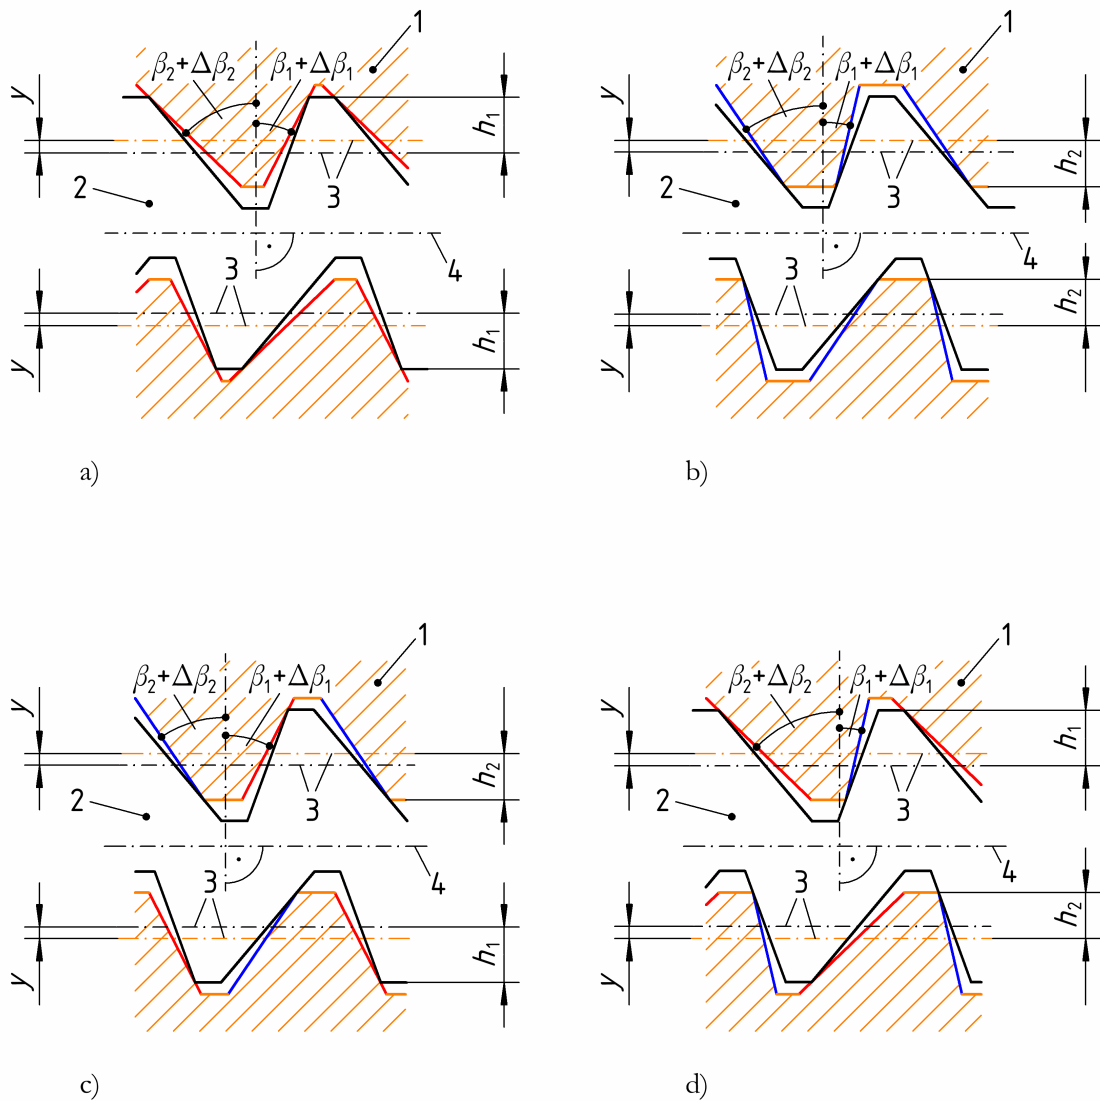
aus den Gewindeflankenwinkelabweichungen resultierender Paarungsausgleichsbetrag eines zylindrischen Außengewindes bei Vorliegen der Gewindeflankenwinkelabweichungen a) über die gesamte Einschraublänge und b) über einen Teil der Einschraublänge
